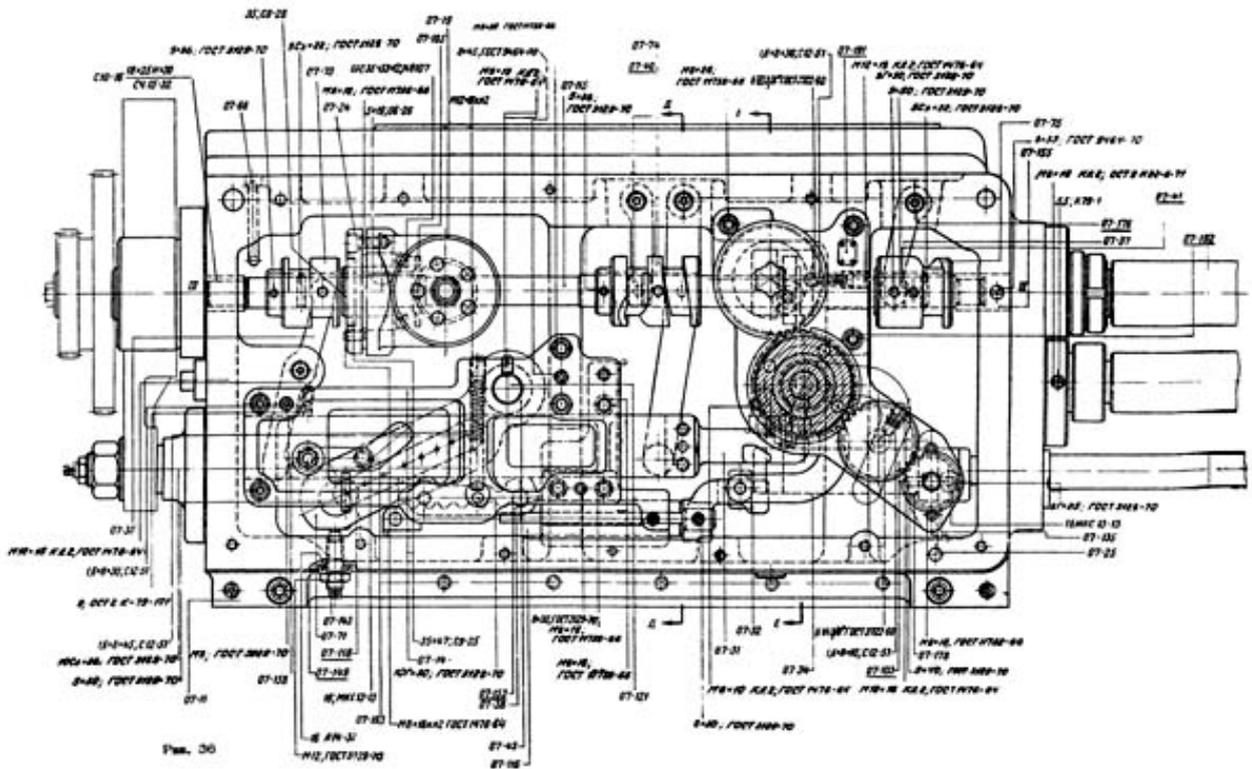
Коробка подач токарного верстата 1Б240П-6К
